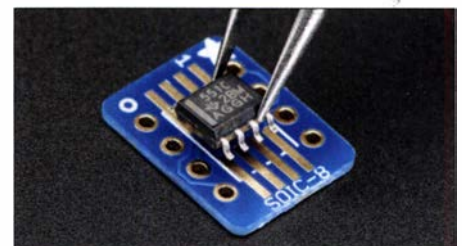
Adapterplatine von Adafruit für SMD-Bauteile im SOIC-8-Gehäuse
